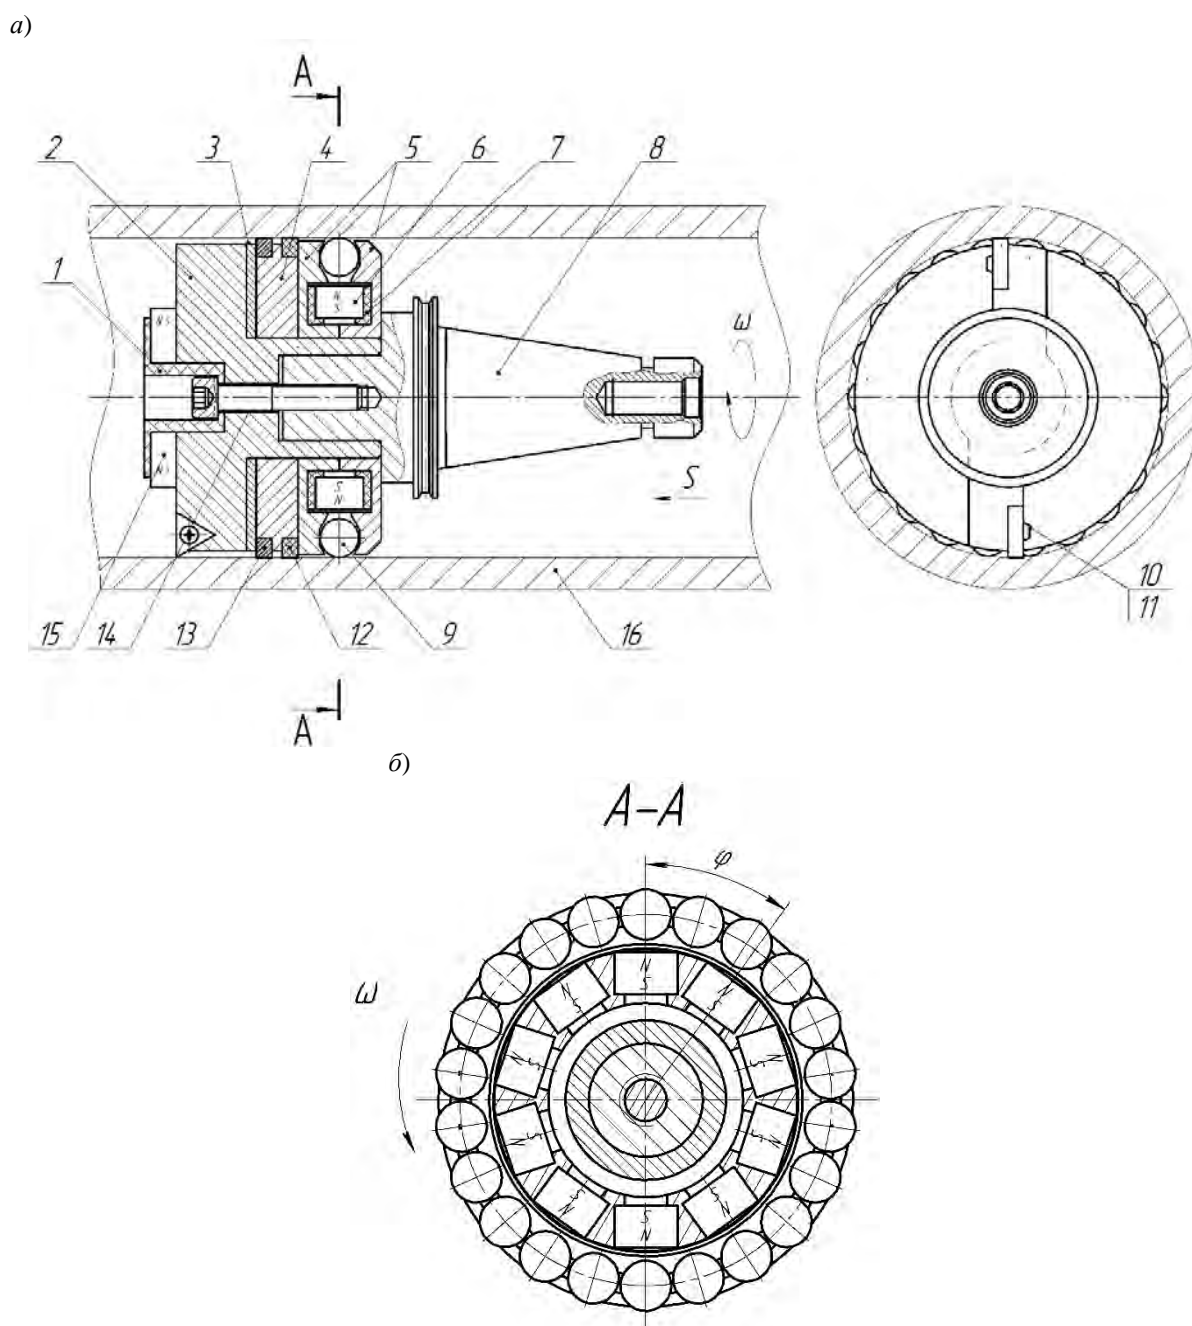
Конструкция инструмента для совмещенной обработки резанием и магнитно-динамическим раскатыванием: а – общий вид; б – поперечное сечение инструмента
